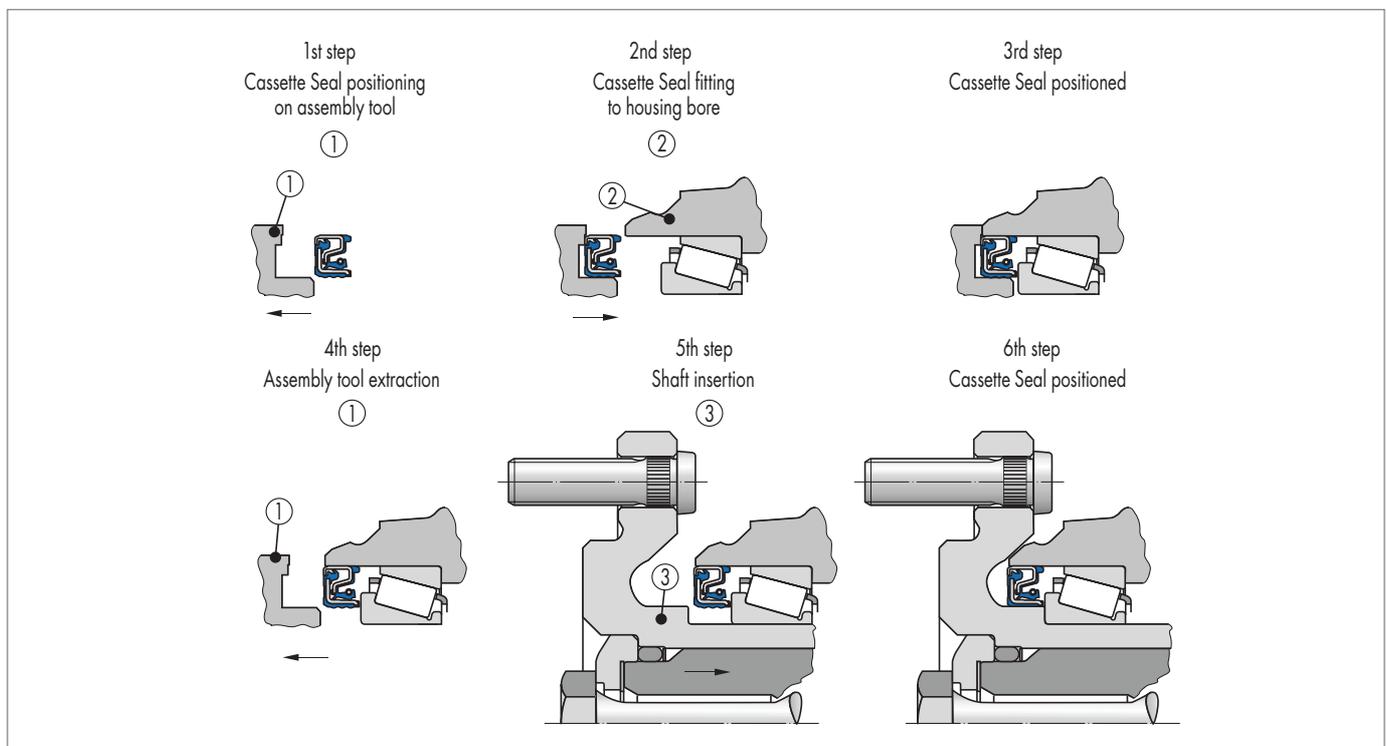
Montage von Simmering Cassette Seal – Fall A (mit „bearing stop“) / Yağ Halkası Cassette Seal Montajı – Durum A („bearing stop“ ile) / Montaż uszczelnienia typu kaseta – przykład A (z „bearing stop“) / Монтаж кассетного уплотнения – вариант А (с «упором в подшипник»)
